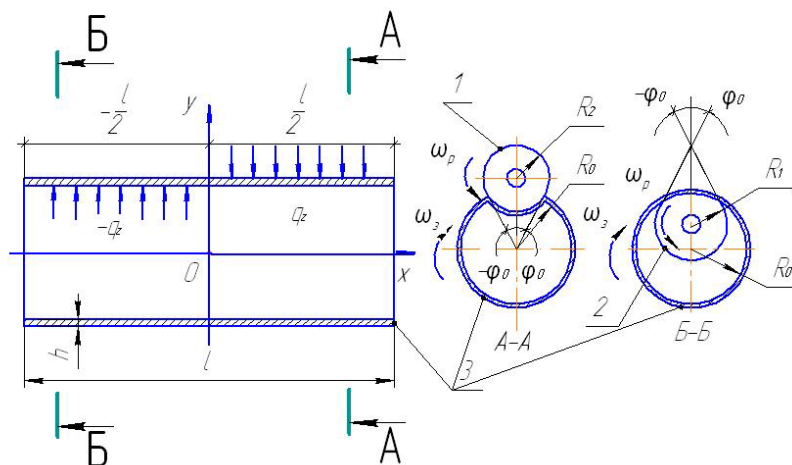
Расчетная схема при профилировании цилиндрической заготовки в обод (1 – верхний ролик, 2 – нижний ролик, 3 – заготовка)
